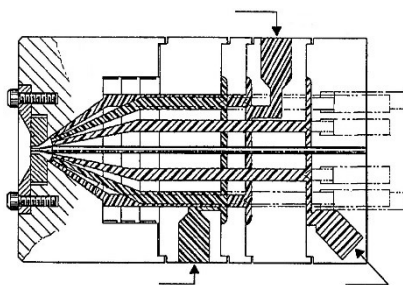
Головка для формування тришарової трубчастої заготовки (заявка № WO95/29051A1)
